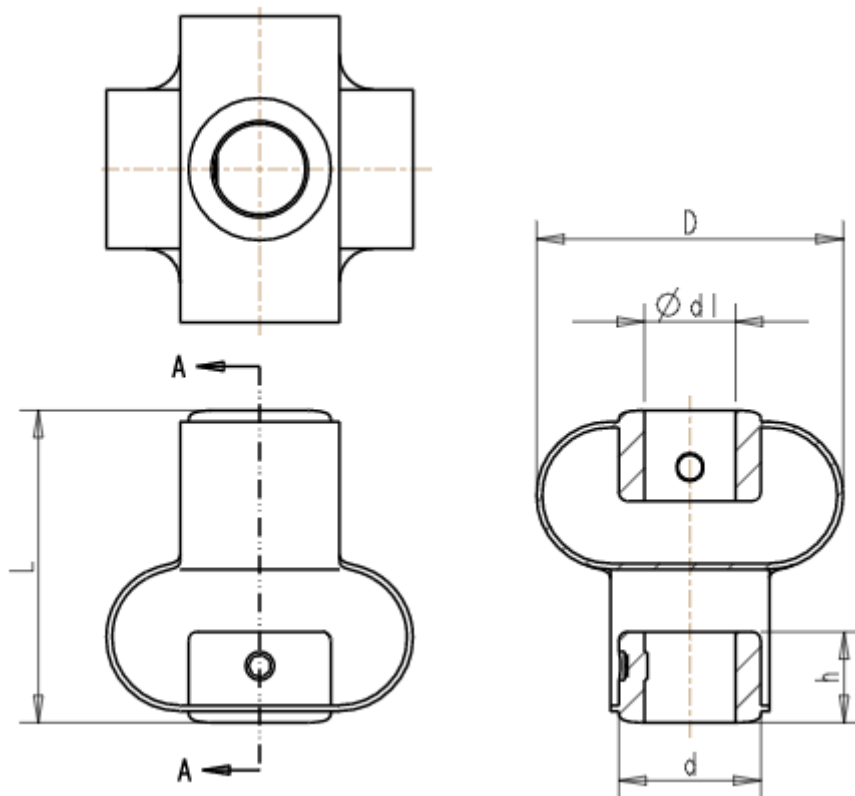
Alzado, planta y sección del acoplamiento elástico utilizado
